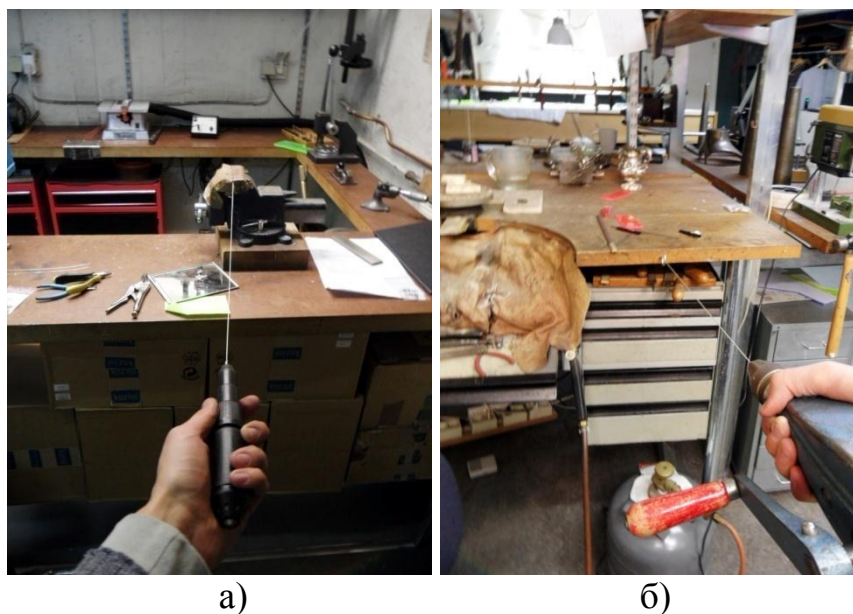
Процесс изготовления веревочки: а – правка проволоки натяжением; б – скручивание веревочки при помощи ручной дрели
